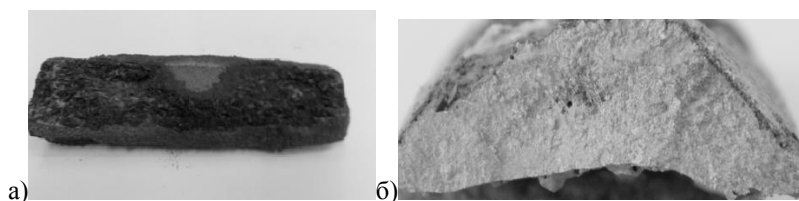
Внешний вид (а) и излом (б) шихтовой заготовки полученной путем заливки металла в изложницы с расплавляемой футеровкой
